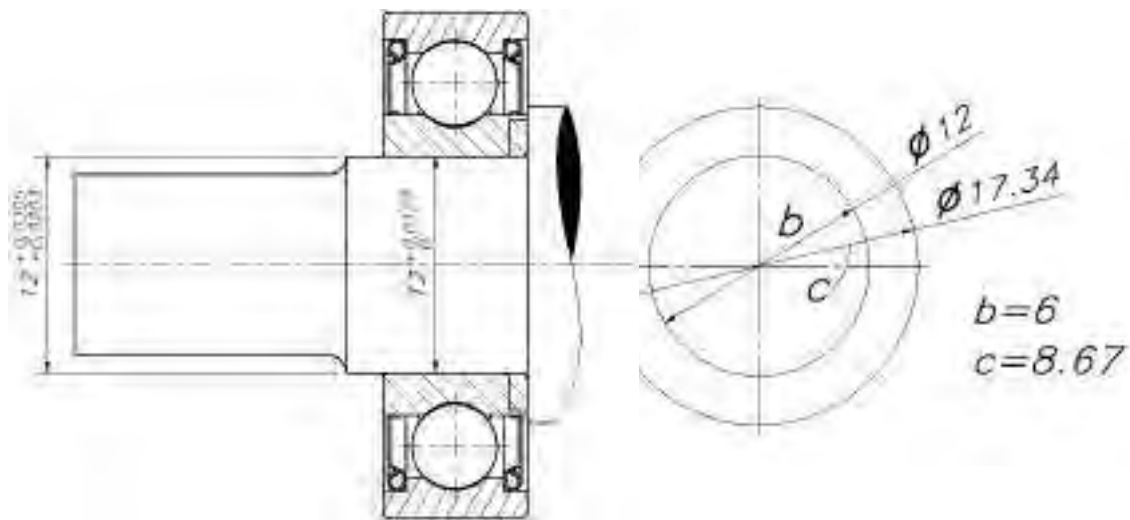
Tolerancia en eje y rodamiento Fuente: Propia
